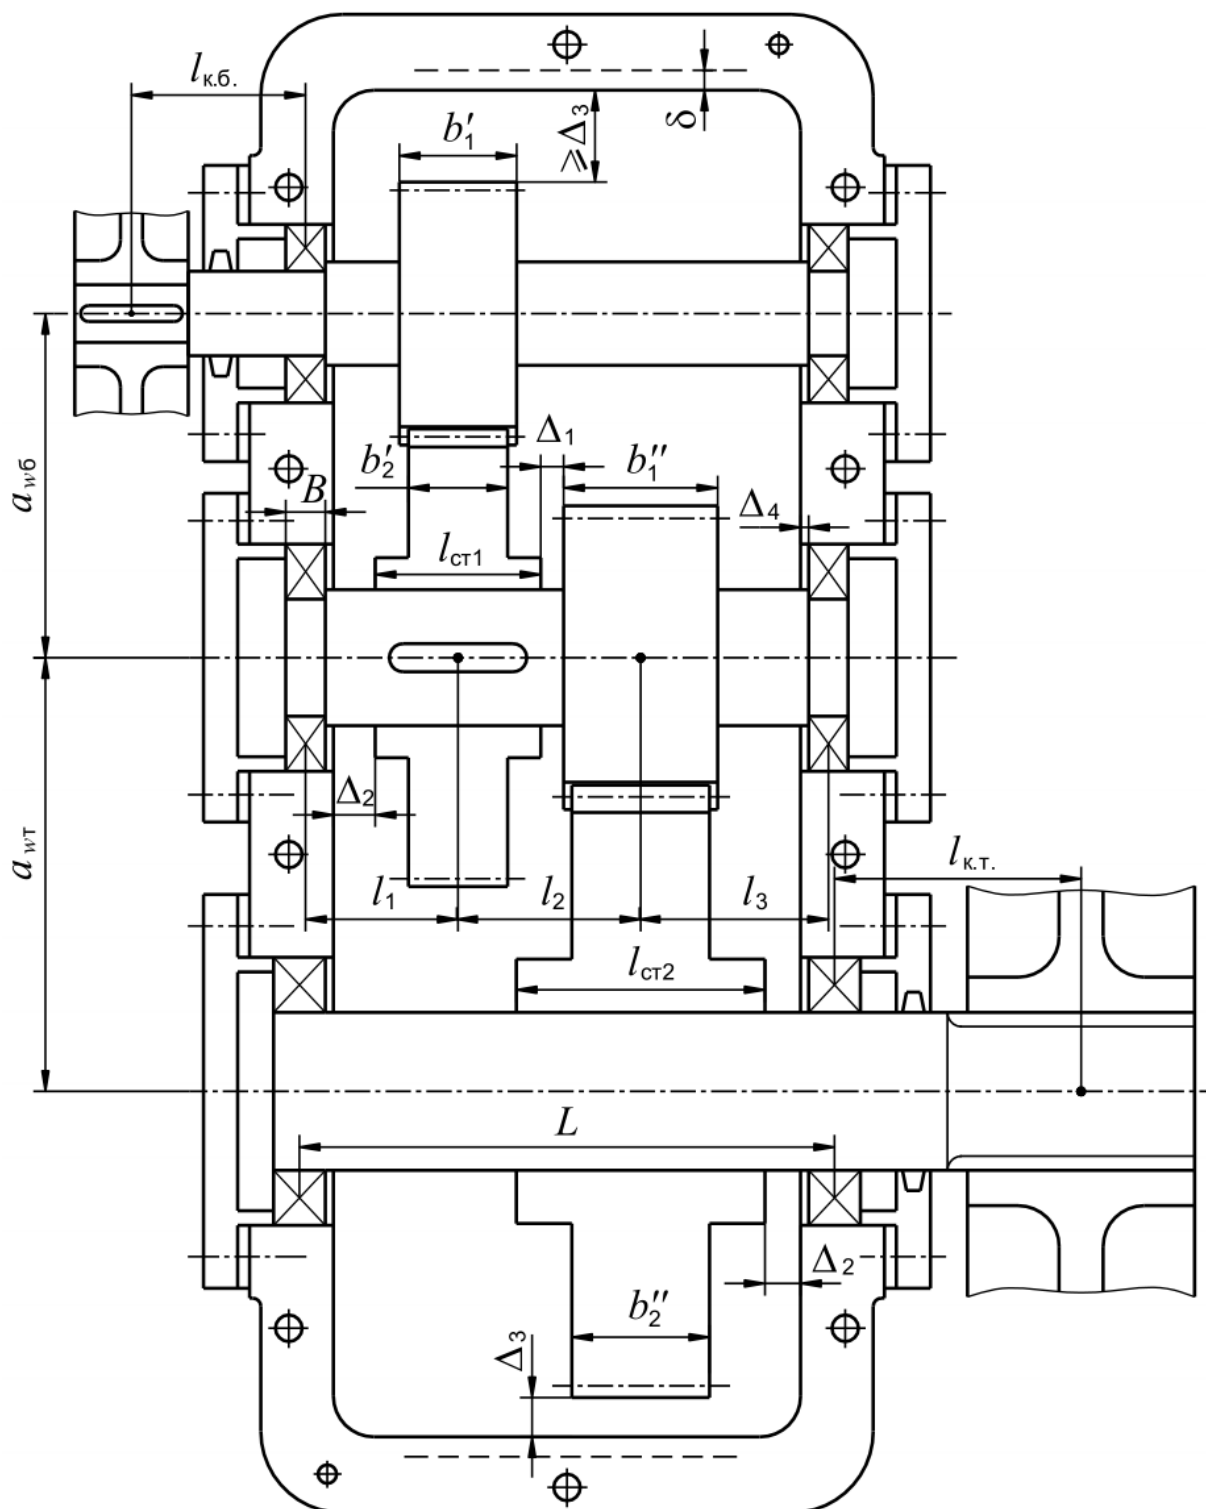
Эскизная компоновка двухступенчатого цилиндрического редуктора
